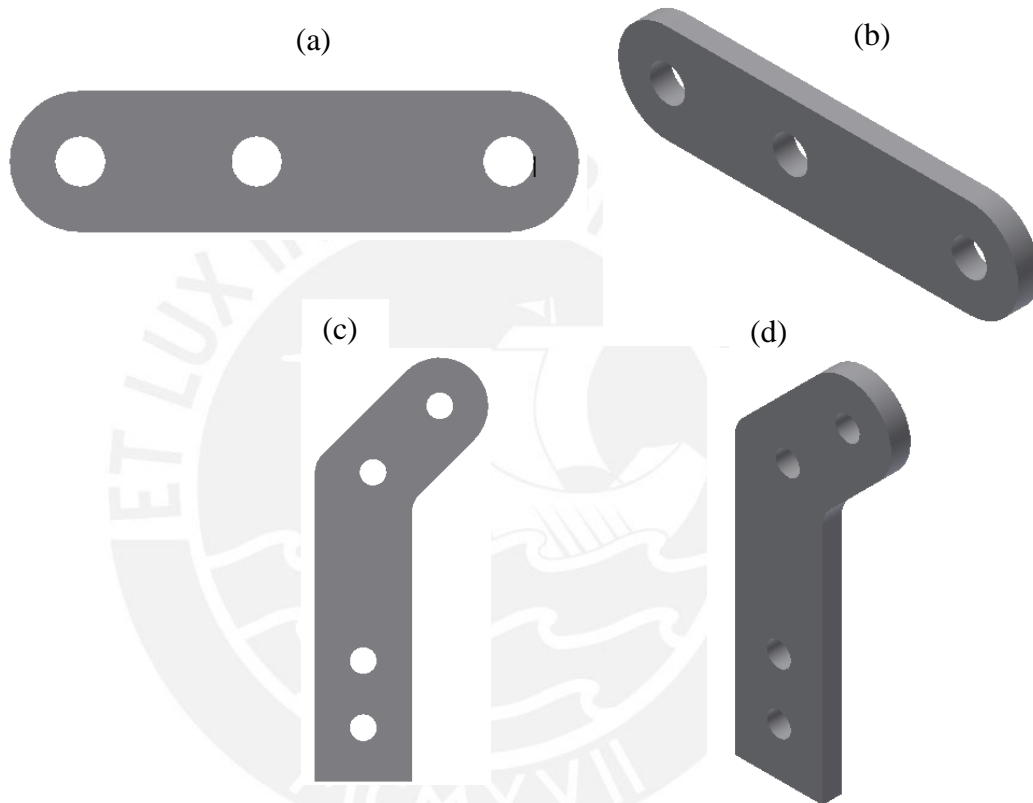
(a) (b) Pieza de unión del actuador lineal/ Pieza L Vistas frontal e isométrica, (c) (d) Pieza L de unión del asiento/apoyapié/ actuador lineal Vistas frontal e isométrica
